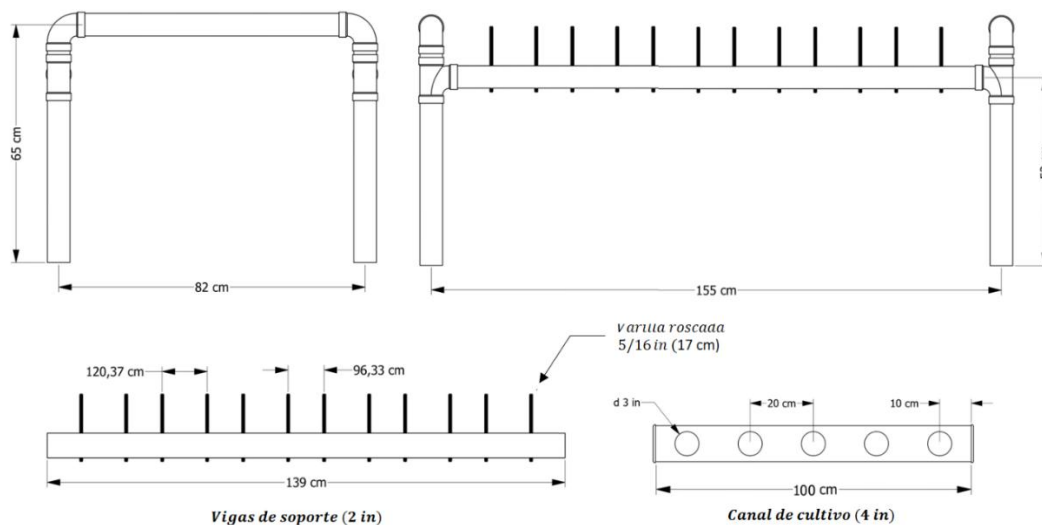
Planos de la estructura, las vigas de soporte y el canal de cultivo para el sistema de Inundación y Drenaje. Fuente: (Rosero, 2019)
